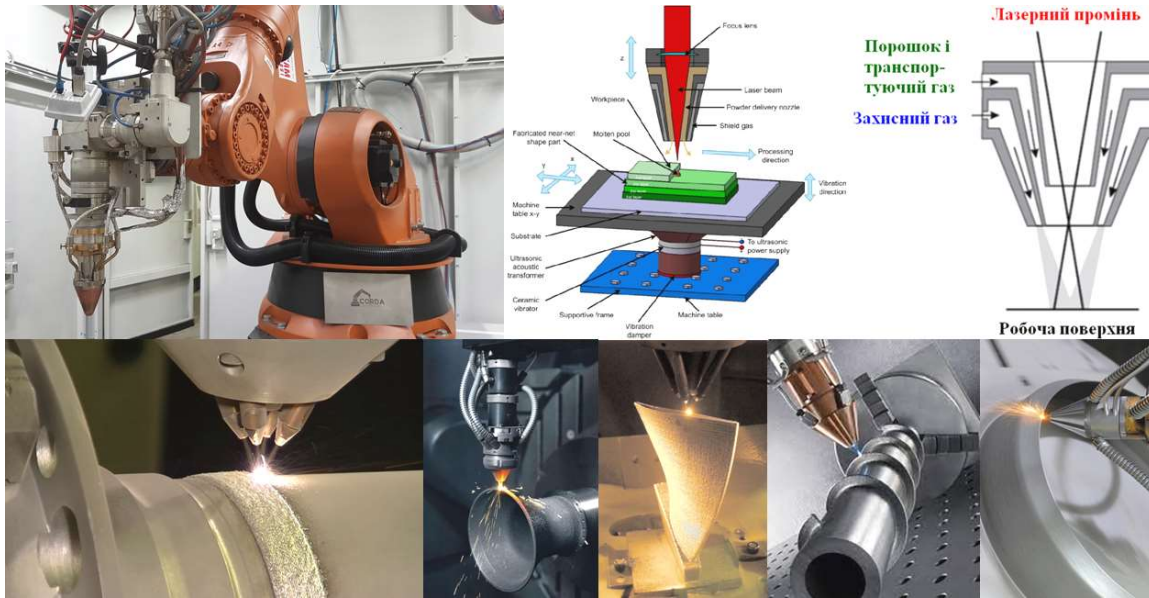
АТ газопорошкової лазерної плавки та її вироби
